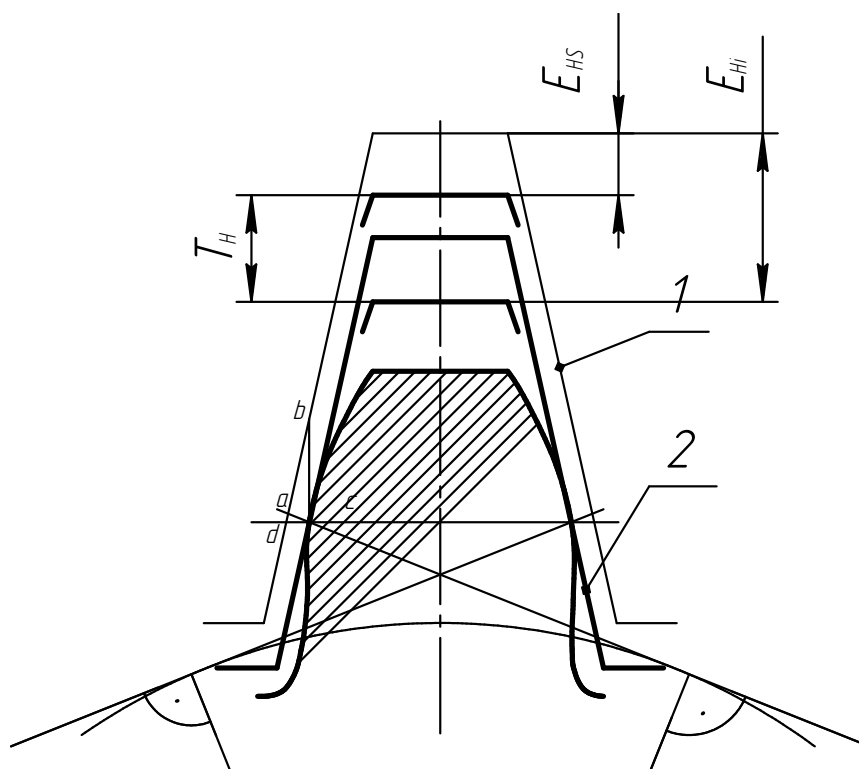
Исходный контур зуборезного инструмента:
